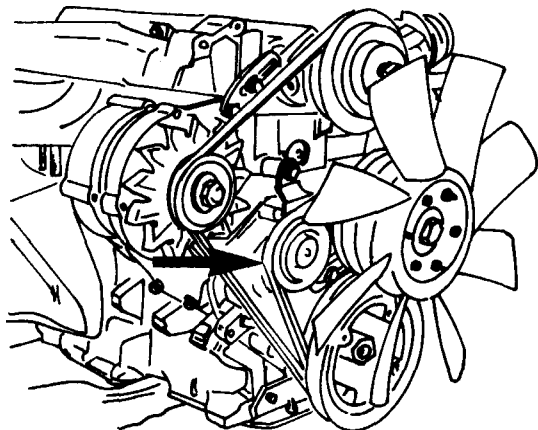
Стрелка указывает натяжной ролик клинового ремня вентилятора.
